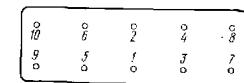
Последовательность затяжки гаек крепления головки цилиндров
